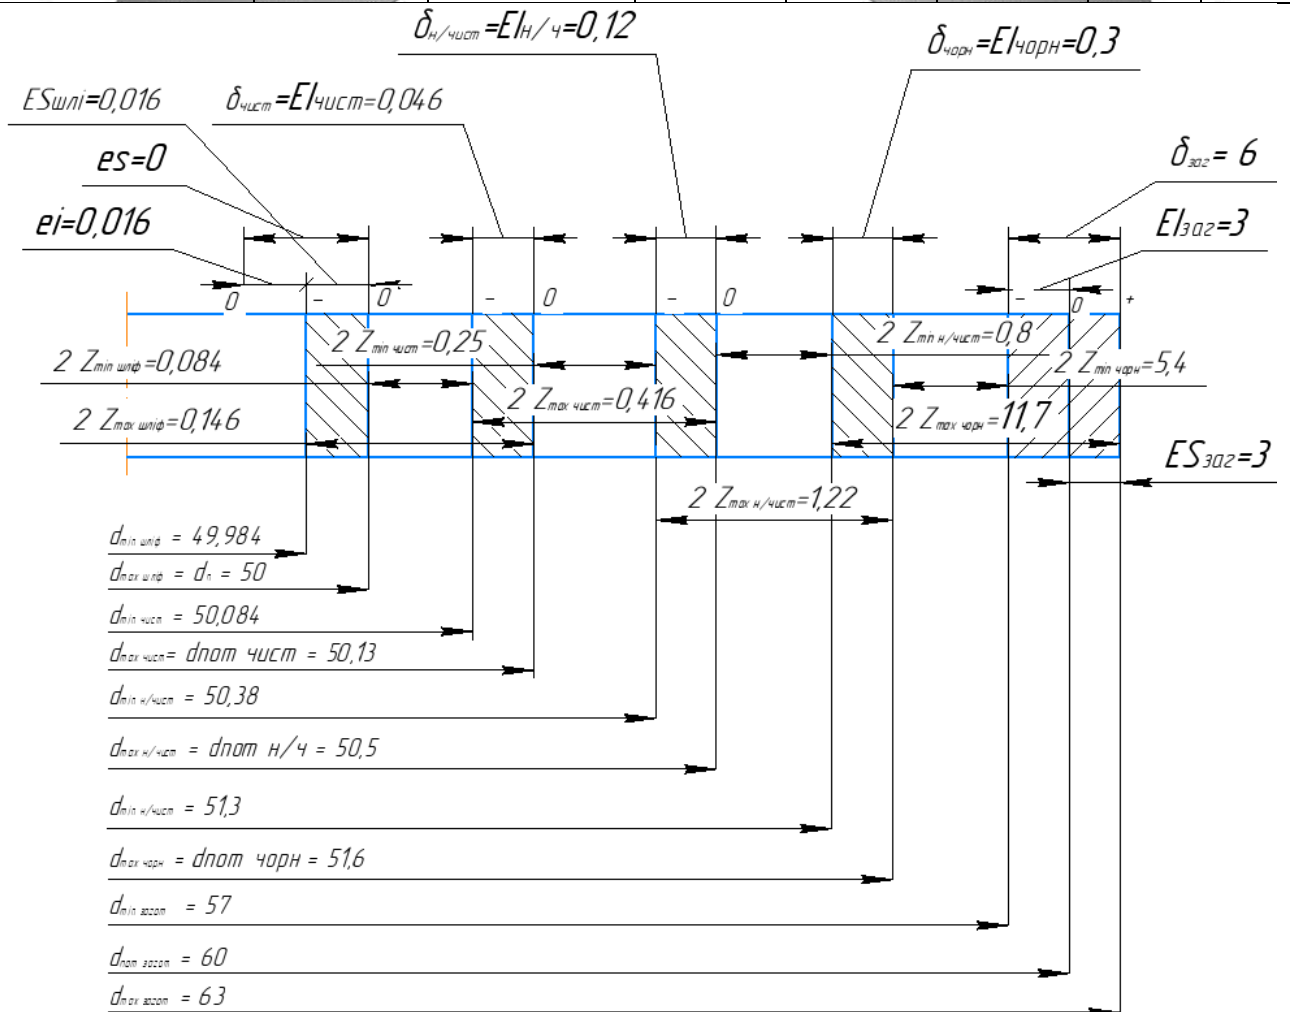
Схема розташування припусків і допусків на обробку діаметрального розміру Ø50h6
